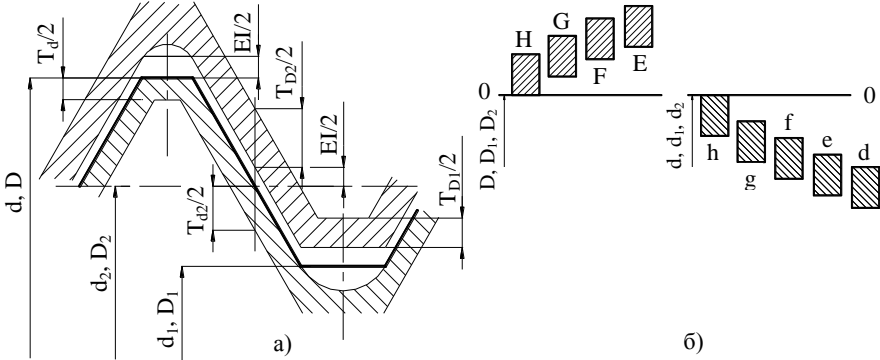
Посадка із зазором метричної різьби: а) схема полів допусків; б) основні відхилення
